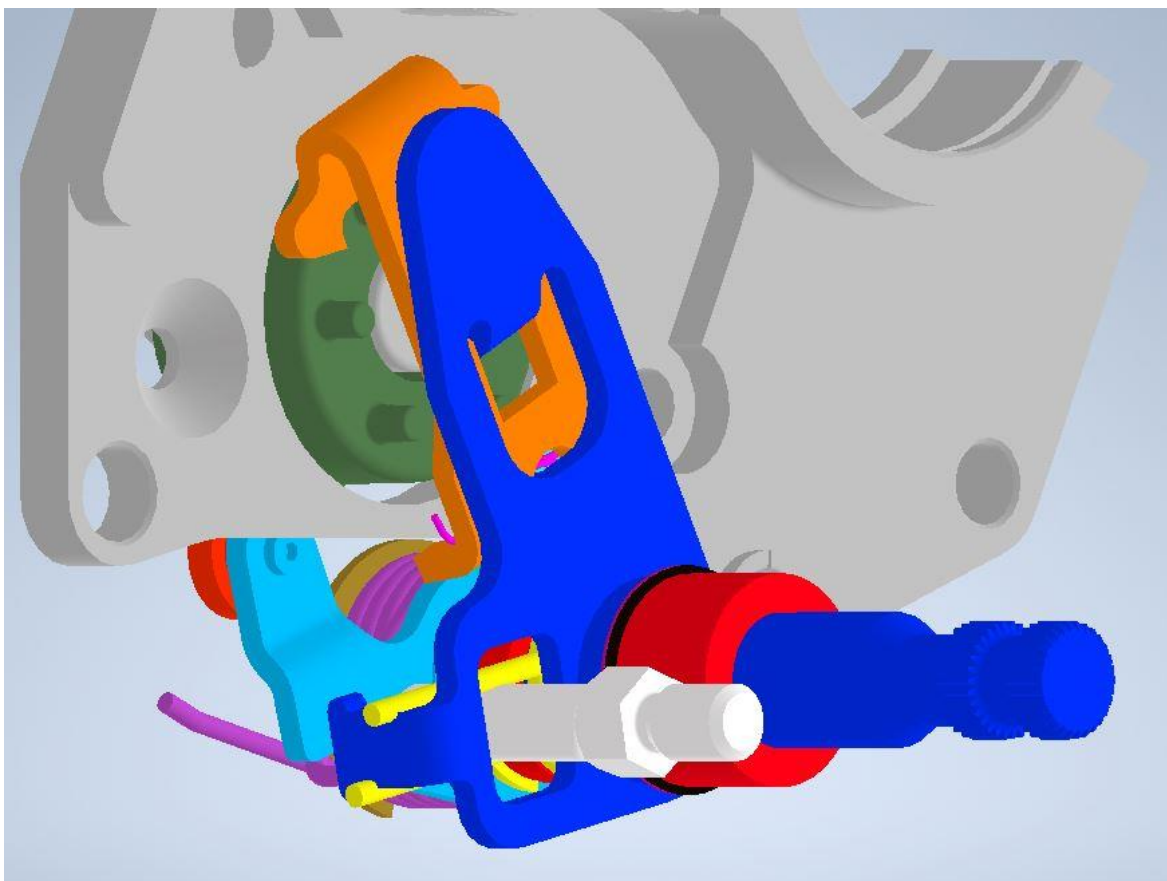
Rozpad aktuálního mechanismu řazení Jawa
